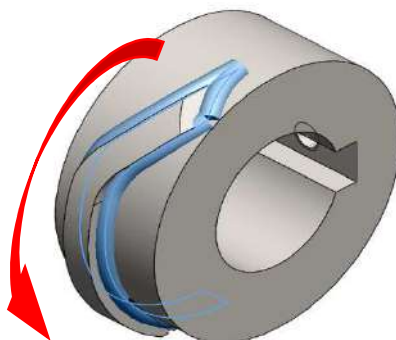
Unión soldada en Porta navaja rotatorio.
